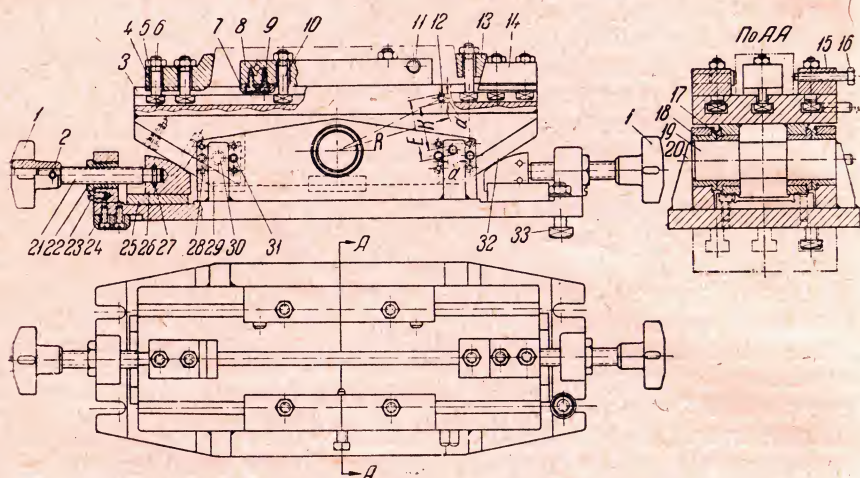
Приспособление для фрезерования обеих сторон рифлений ножей сборных разверток.
